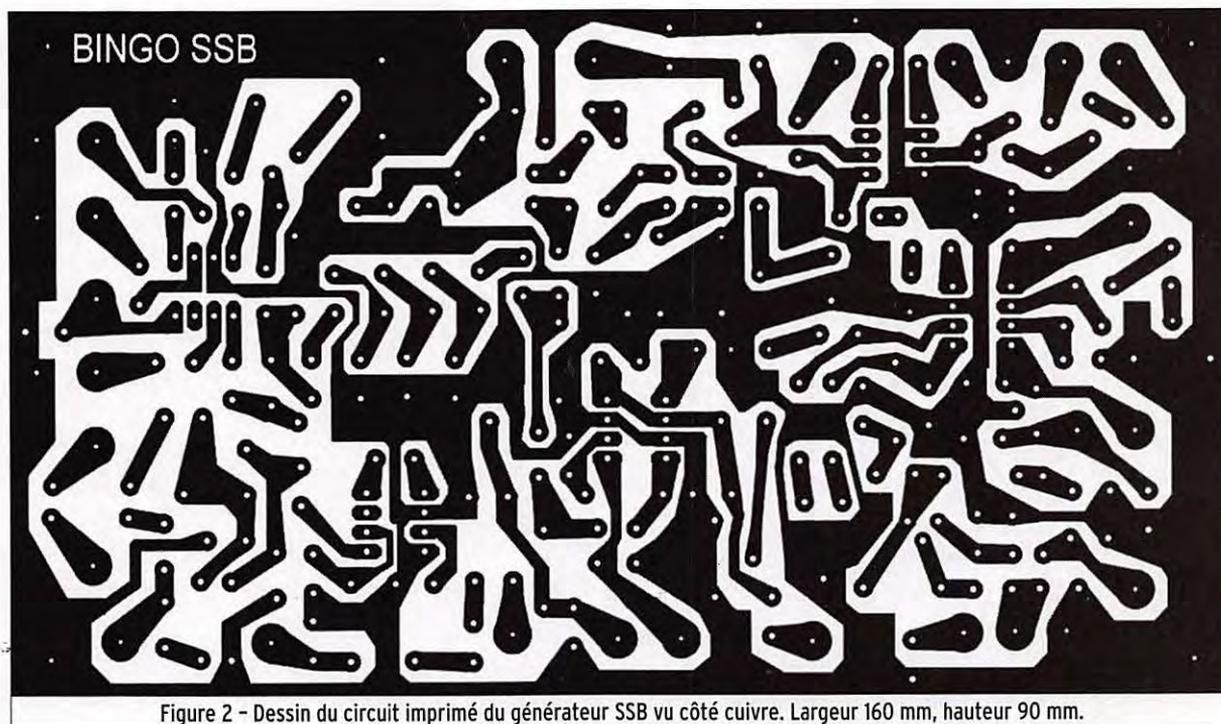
Dessin du circuit imprimé du générateur SSB vu côté cuivre. Largeur 160 mm, hauteur 90 mm.
